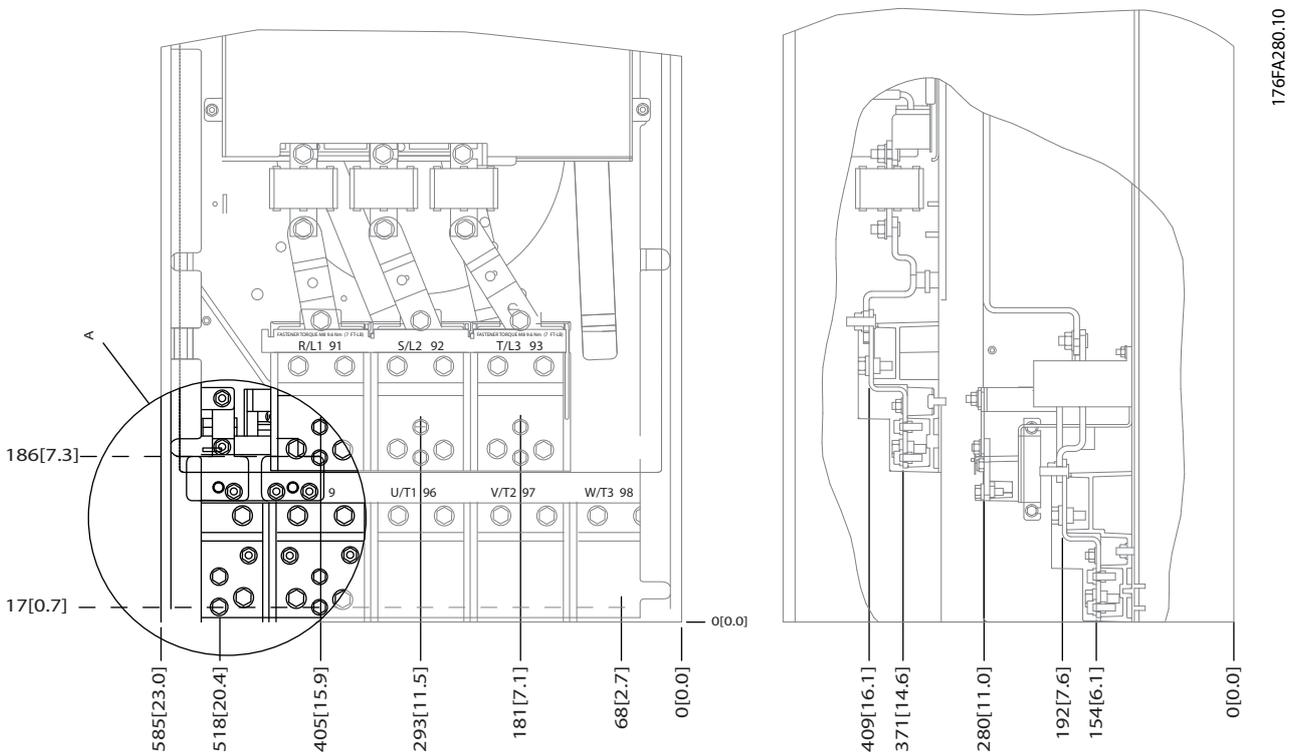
Posiciones de la conexión eléctrica en protecciones IP00
